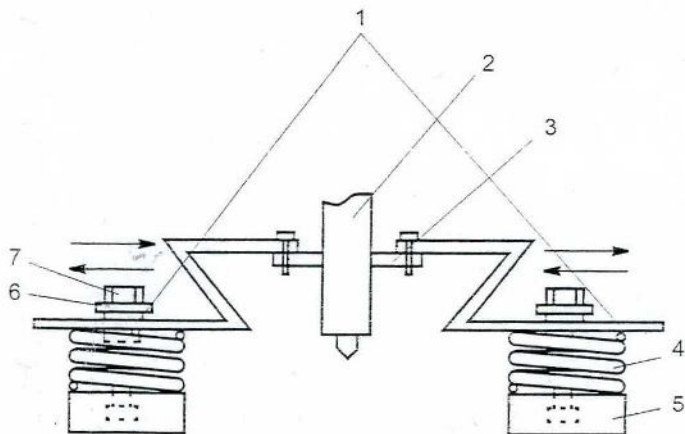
Экспериментальная модель разделенного токоподвода: 1 — стальное основание; 2 — корпус сварочной горелки; 3 — изолятор; 4 — стальные пружины; 5 — графитовые контакты токоподвода; 6 — клемма провода; 7 — болт и гайка
